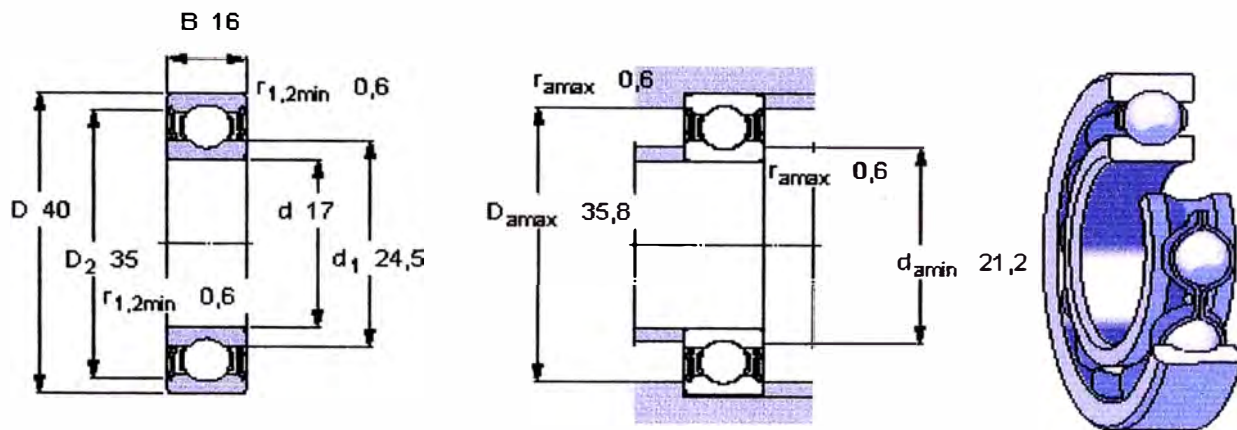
Dibujo y dimensiones del rodamiento de bolas.
